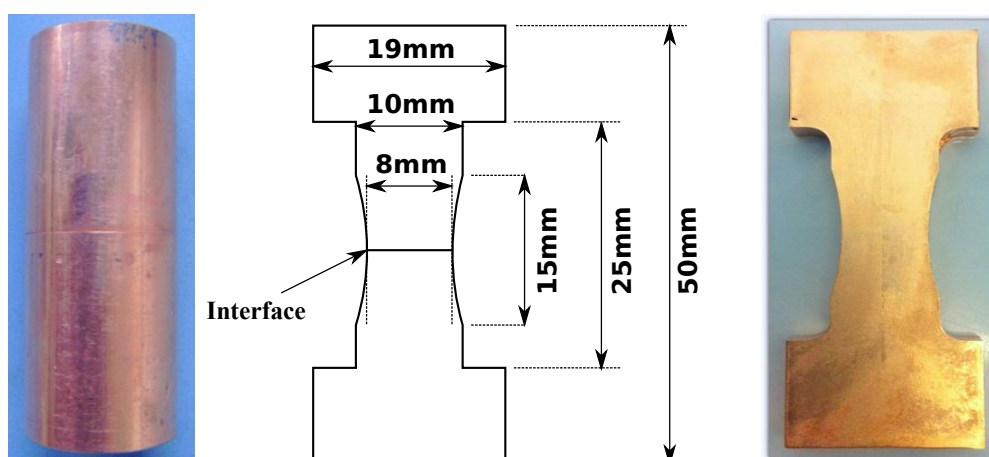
À gauche : une photo des échantillons assemblés (avant usinage), au milieu : les dimensions de l'éprouvette plate et à droite : photo de l'éprouvette de cuivre usiné. L'épaisseur de l'éprouvette est 6 mm
